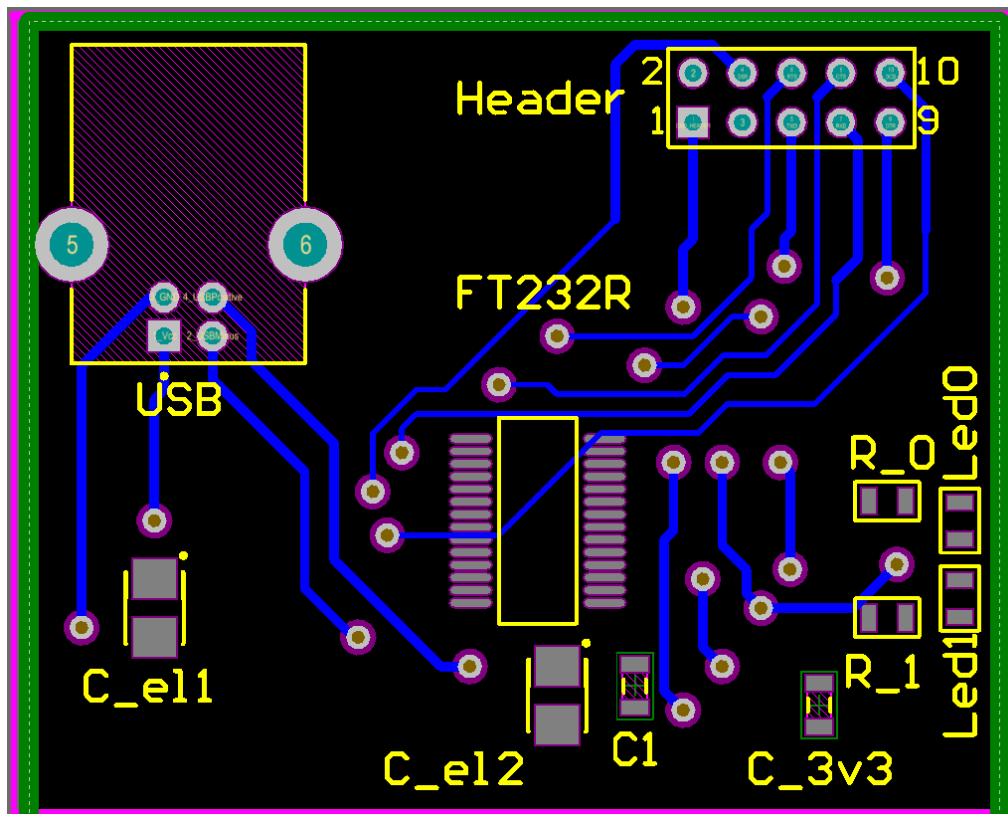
Capa inferior del PCB diseñado en Altium Designer.
